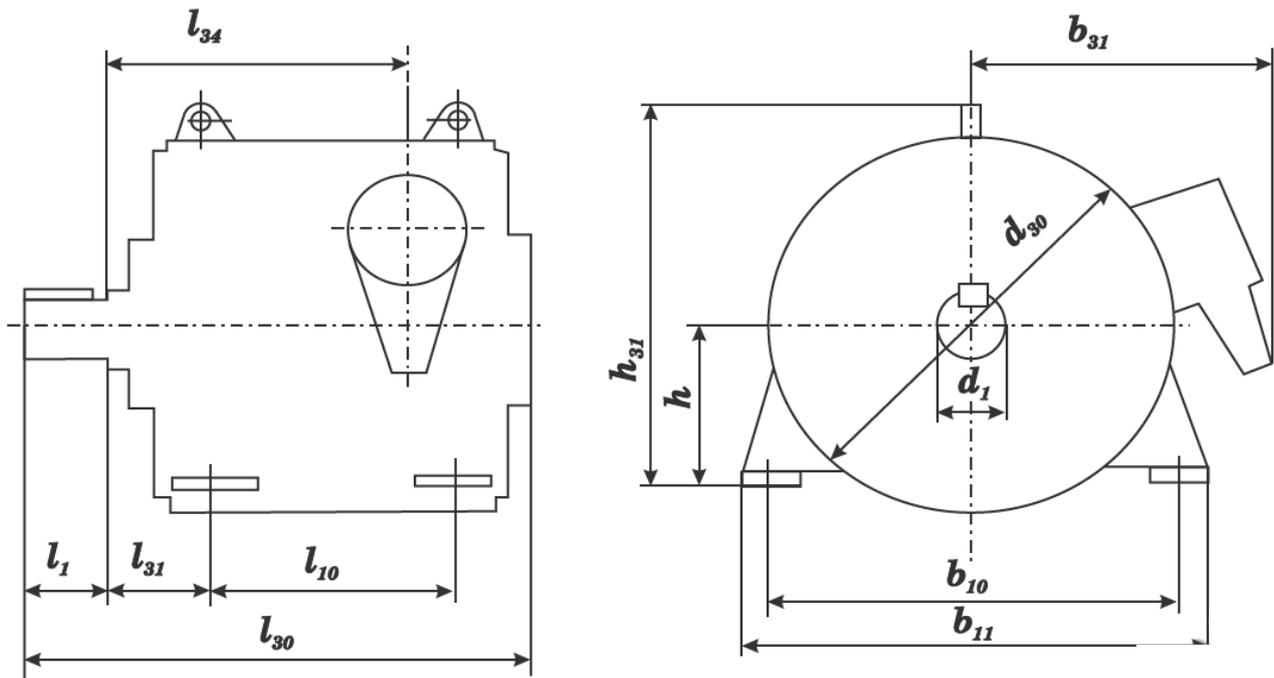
Габаритные, установочные, присоединительные размеры двигателей АН-4
